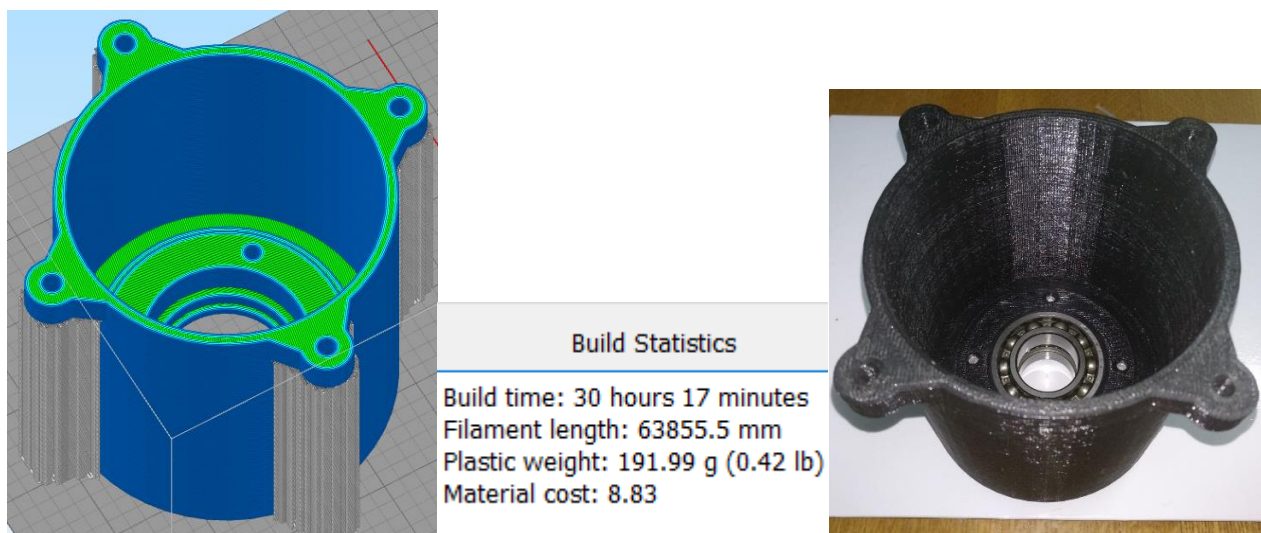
Моделювання процесу 3D-друку лівої кришки – зовнішнього корпусу редуктора та отримані деталі
